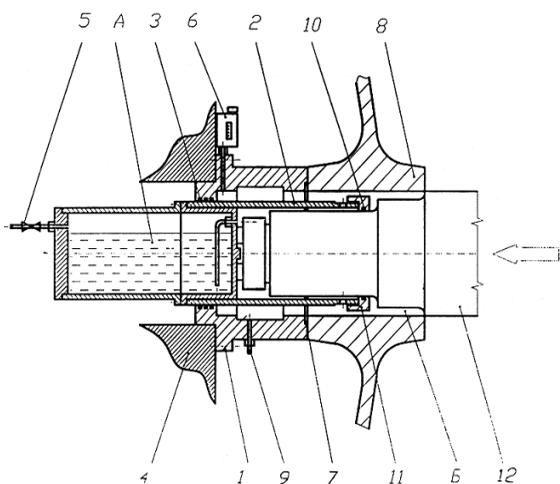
Устройство для смазки поверхностей сопряжения осей и колёс при механической запрессовке колёсных пар
